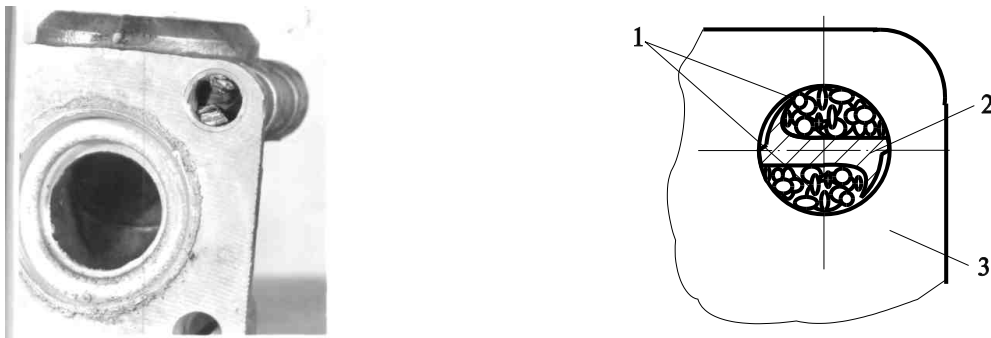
Характерна поломка гвинтового свердла $\varnothing 11,2$ мм в корпусних деталі через пакетування стружки в стружкових канавках (матеріал заготовки АК7, інструменту Р6М5ФЗ, $V = 31,38$ мм/хв., $S = 0,26$ мм/об., охолодження Аквол 10-М 5...7 л/хв.
